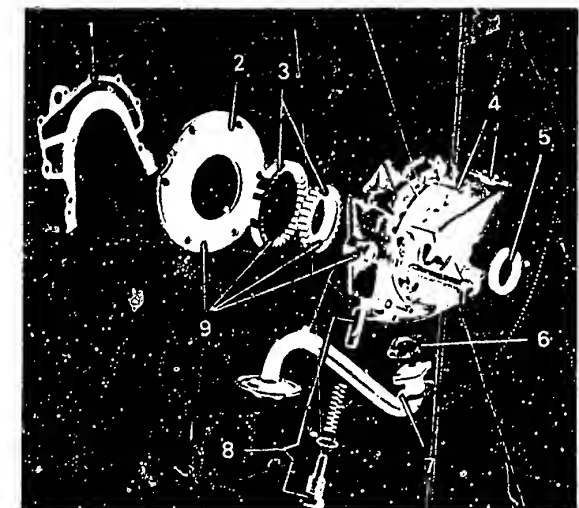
Einzelteile der Sichelölpumpe: 1 Dichtung – 2 Abschlussplatte – 3 Aussen- und Innenzahnrad – 4 dünne Gehäuseschrauben – 5 Simmerring – 6 Flanschdichtung – 7 Saugleitung – 8 Überdruckventil – 9 Teile des Austauschsatzes.
